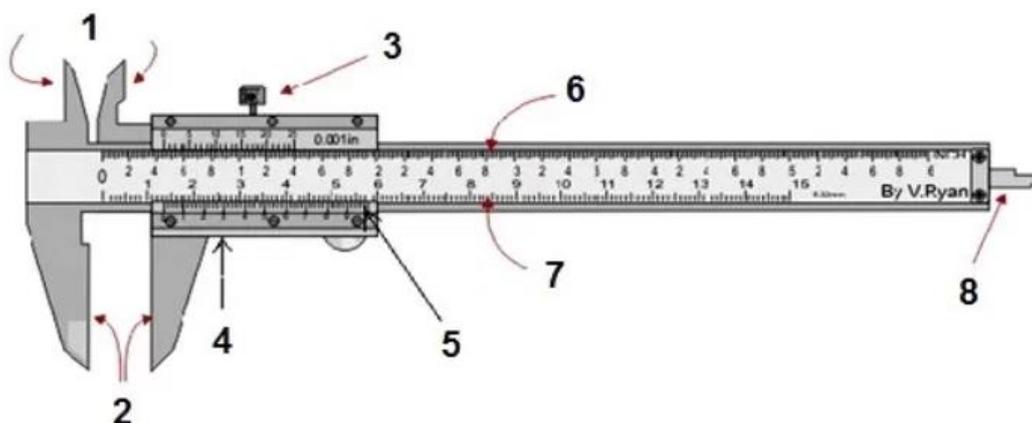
Устройство штангенциркуля: 1 — губки для внутренних измерений; 2 — губки для наружных измерений; 3 — зажимной винт; 4 — подвижная рамка; 5 — нониус; 6 — штанга; 7 — шкала штанги; 8 — глубиномер [2]
